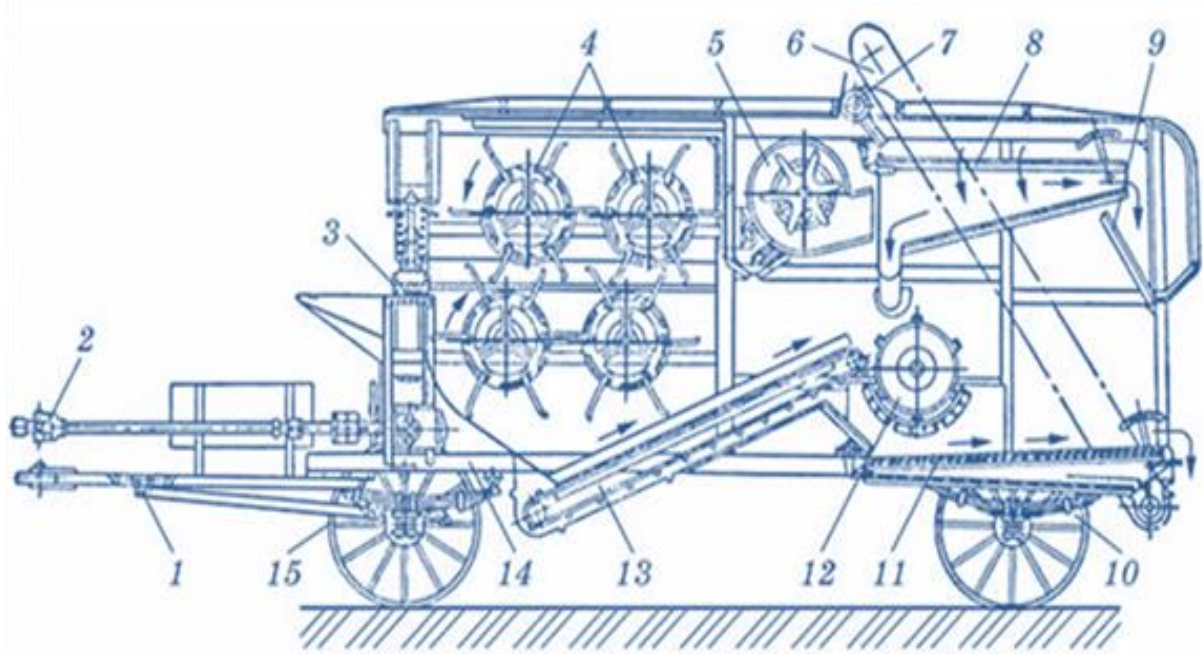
Коноплетарка МЛК-4,5А: 1 – причіпний пристрій; 2 – карданна передача; 3 – затискний конвеєр; 4 – обчісувальний апарат; 5 – вентилятор; 6 – елеватор; 7 – шнек; 8 – решітний стан; 9 – скатна дошка; 10 і 15 – опорні колеса; 11 – грохот; 12 – терковий апарат; 13 – конвеєр вороху; 14 – рама.
